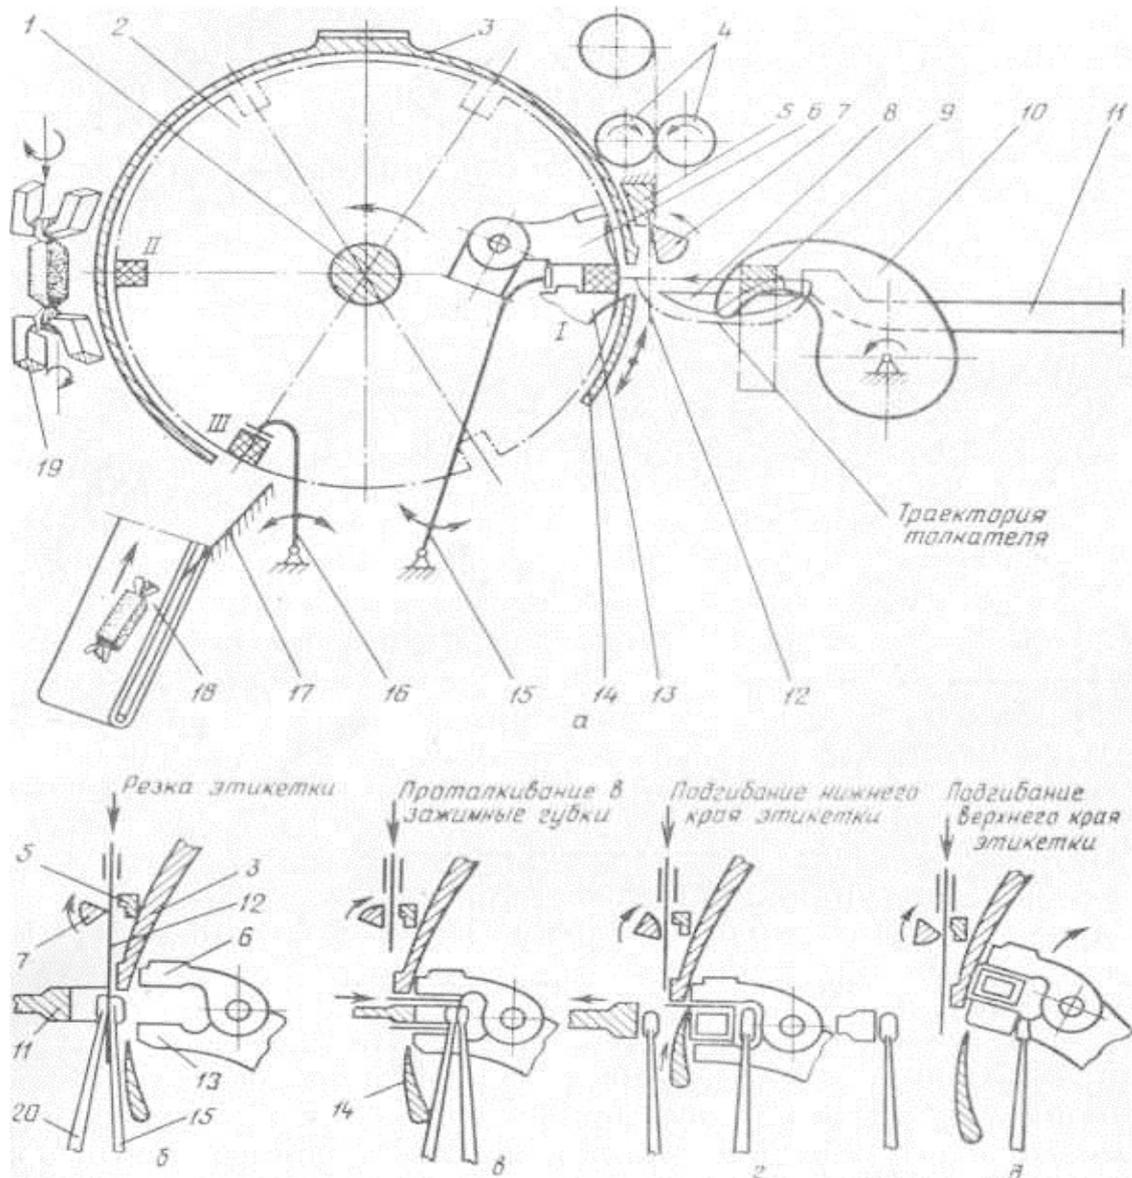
Механический формующий питатель автомата ИЗМ-1 для заправки карамели: а — рабочие позиции ротора; б, в, г, д — последовательность заправки в позиции I ротора
